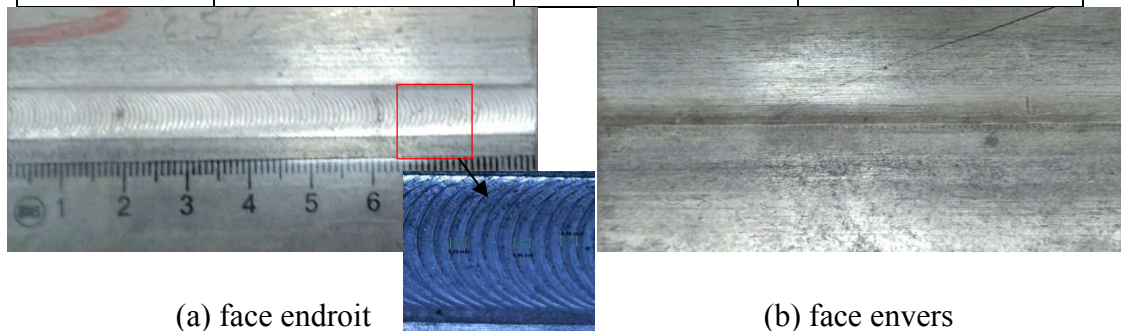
Aspect du cordon de soudure FSW de AZ61-AZ31.
